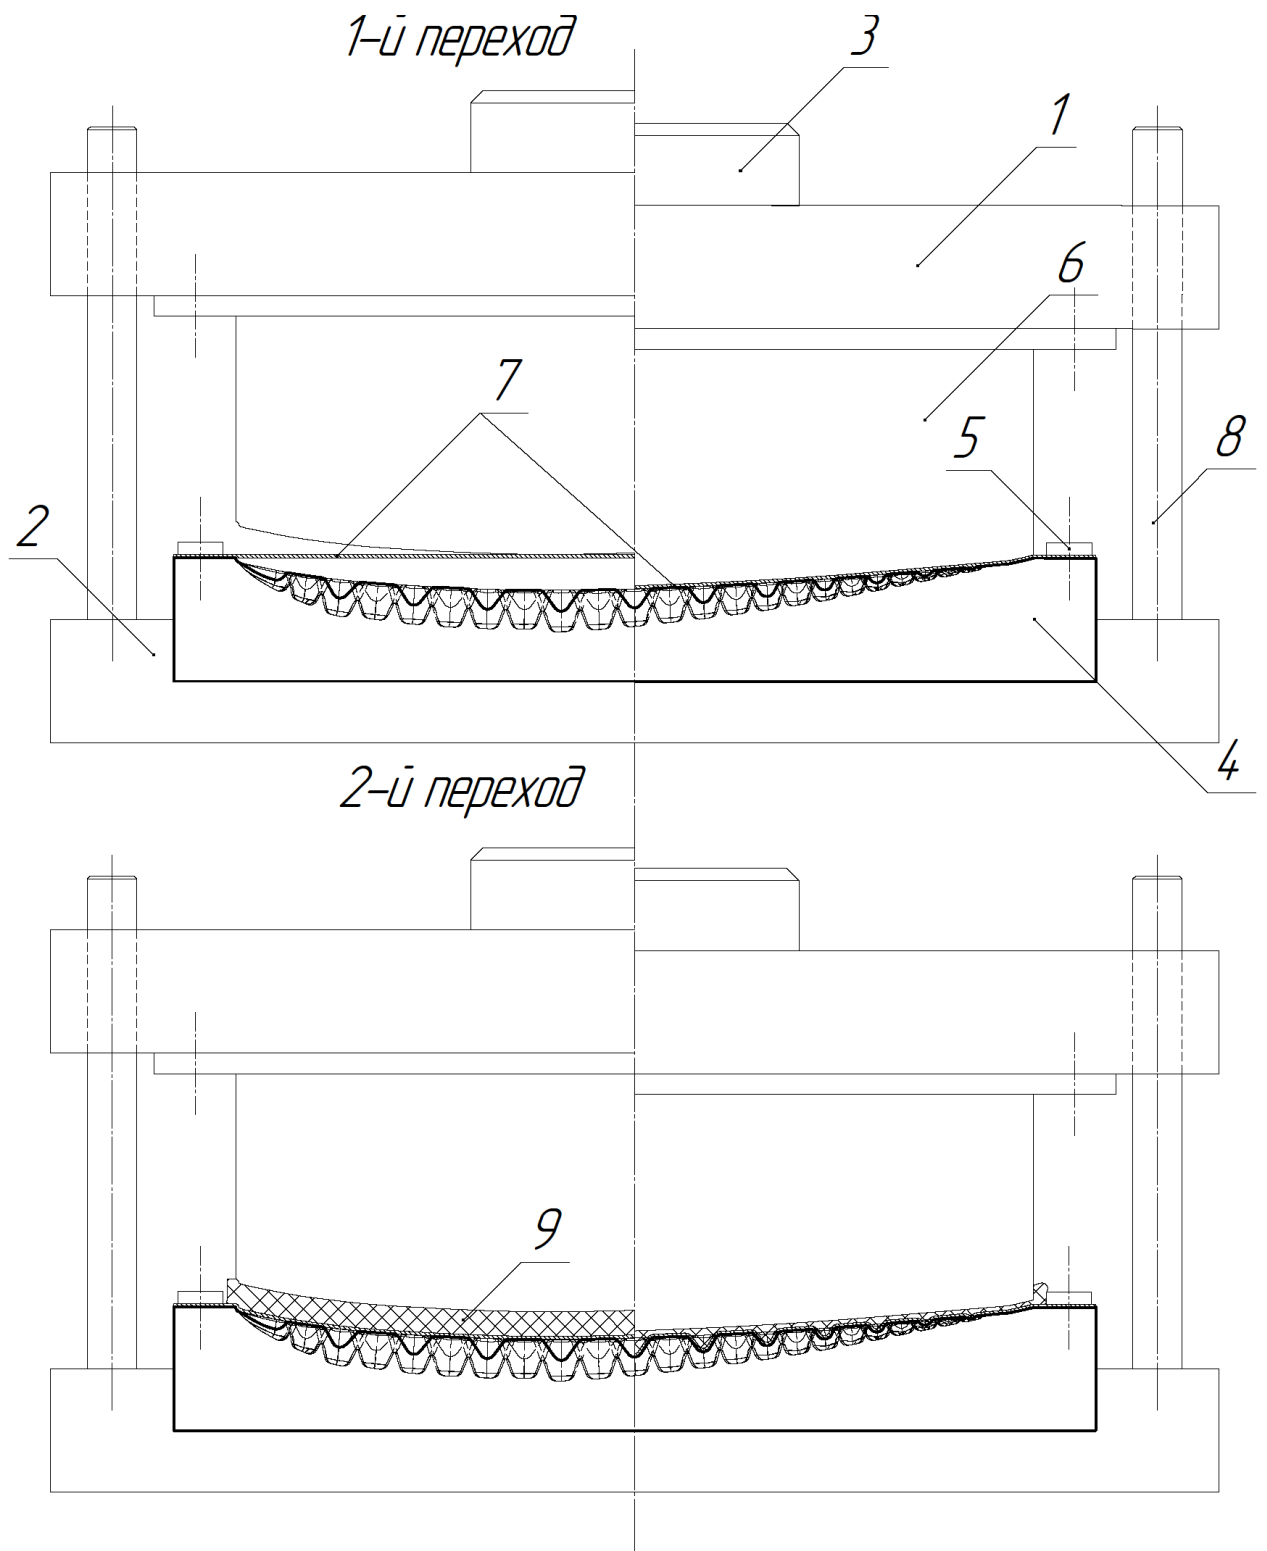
Процесс штамповки дискретного заполнителя закрылка с возможностью УПС
